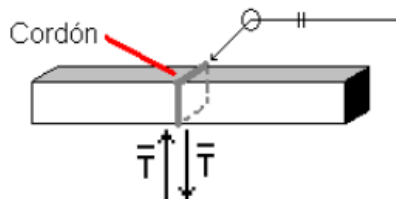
CASO 1 Perímetro soldado [9]
